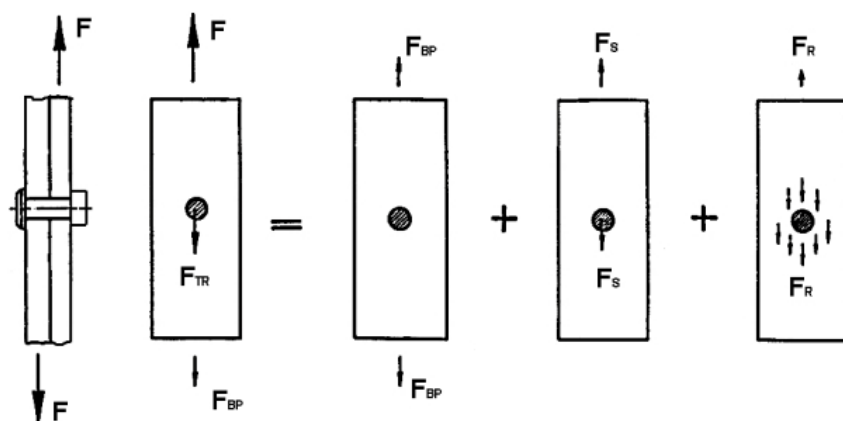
Složení sil v jednoduchém nýtovém spoji [28]
